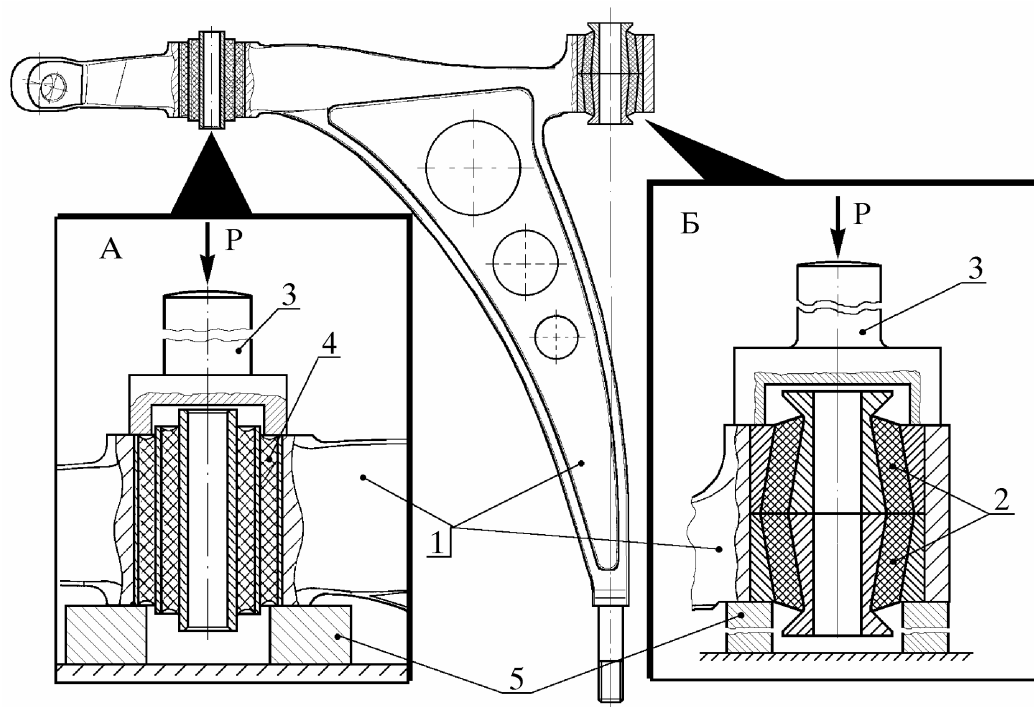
Запрессовка сайлентблока и шарнира амортизатора в отверстия нижнего рычага левого (правого):
